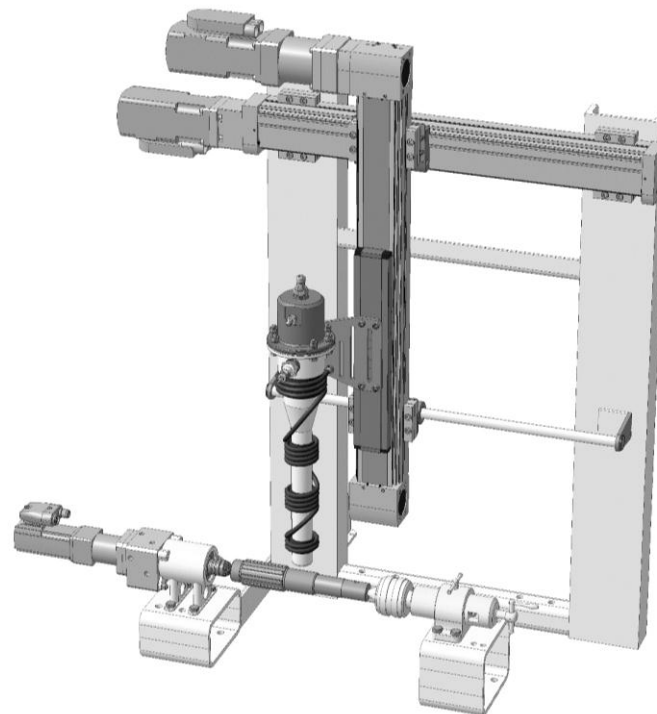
Конструктивна схема установки відновлення
